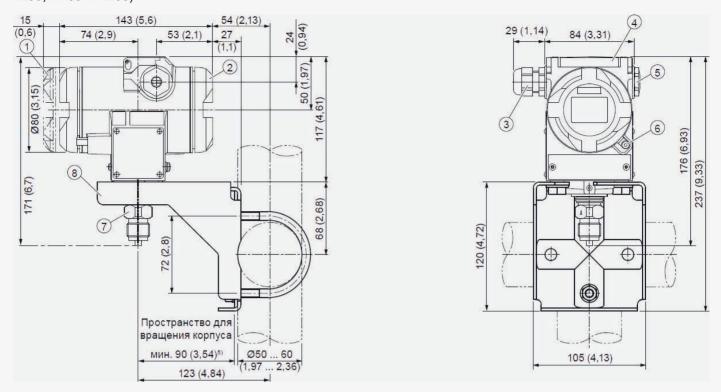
Измерительный преобразователь КМЗ5 в корпусе избыточного давления, размеры в мм (дюймах)
